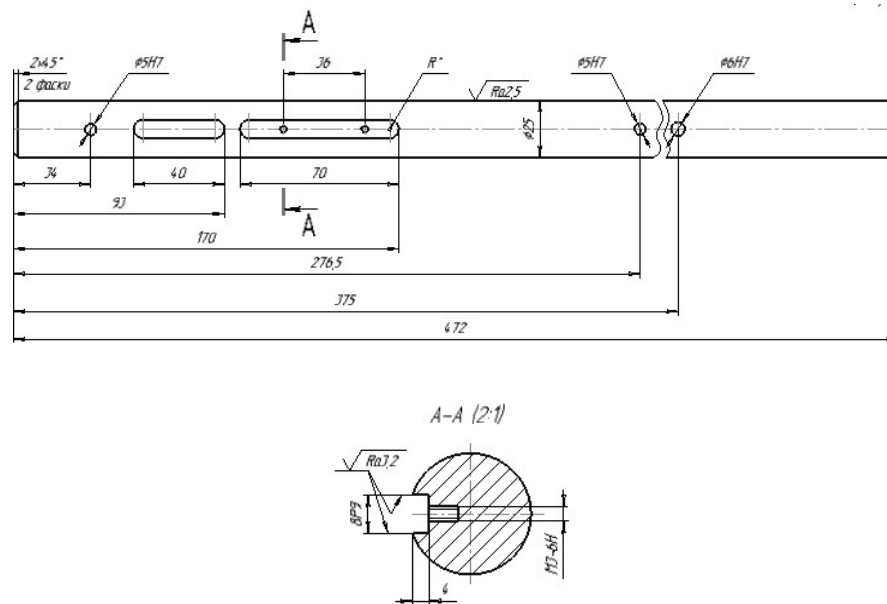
Загальний вигляд конструкції валу ВП.22
